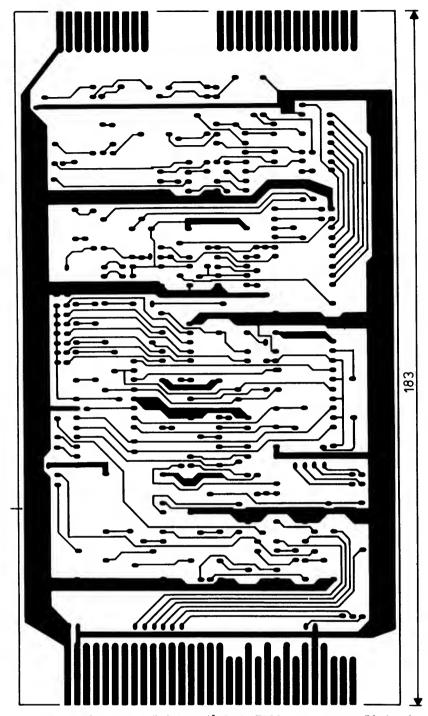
Obrazec plošných spojů desky Z506 - strana bez součástek
